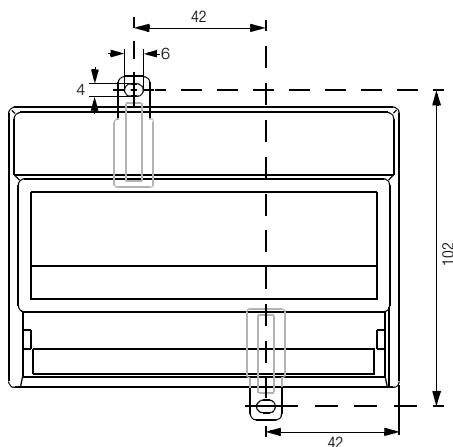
Maßzeichnung für Wandmontage (Frontansicht)
